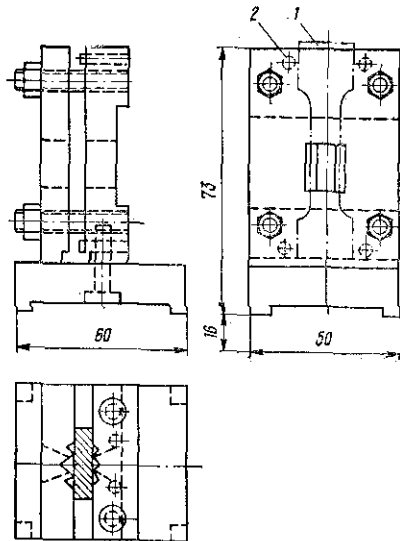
Приспособление для испытания тонких образцов из КМ на сжатие:
